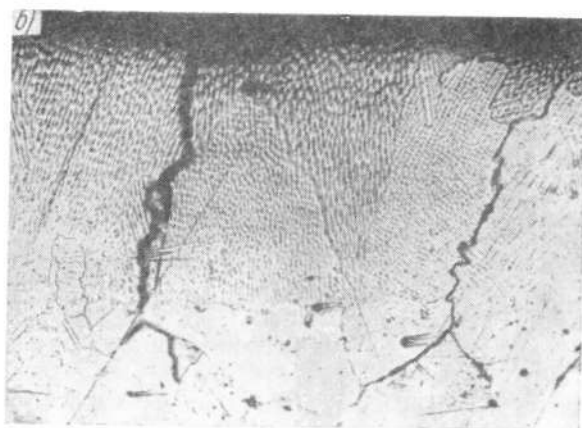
Прижог на границе сплавления металла шва с основным металлом:
